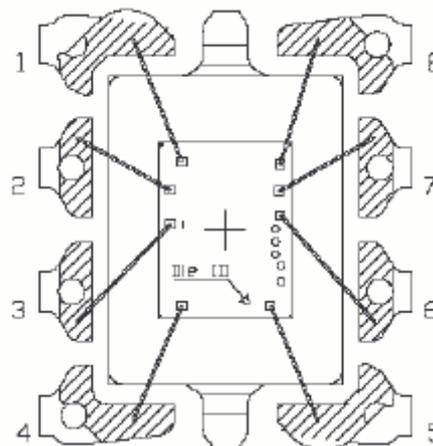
Schéma de l'assemblage après le soudage des fils de connexions
